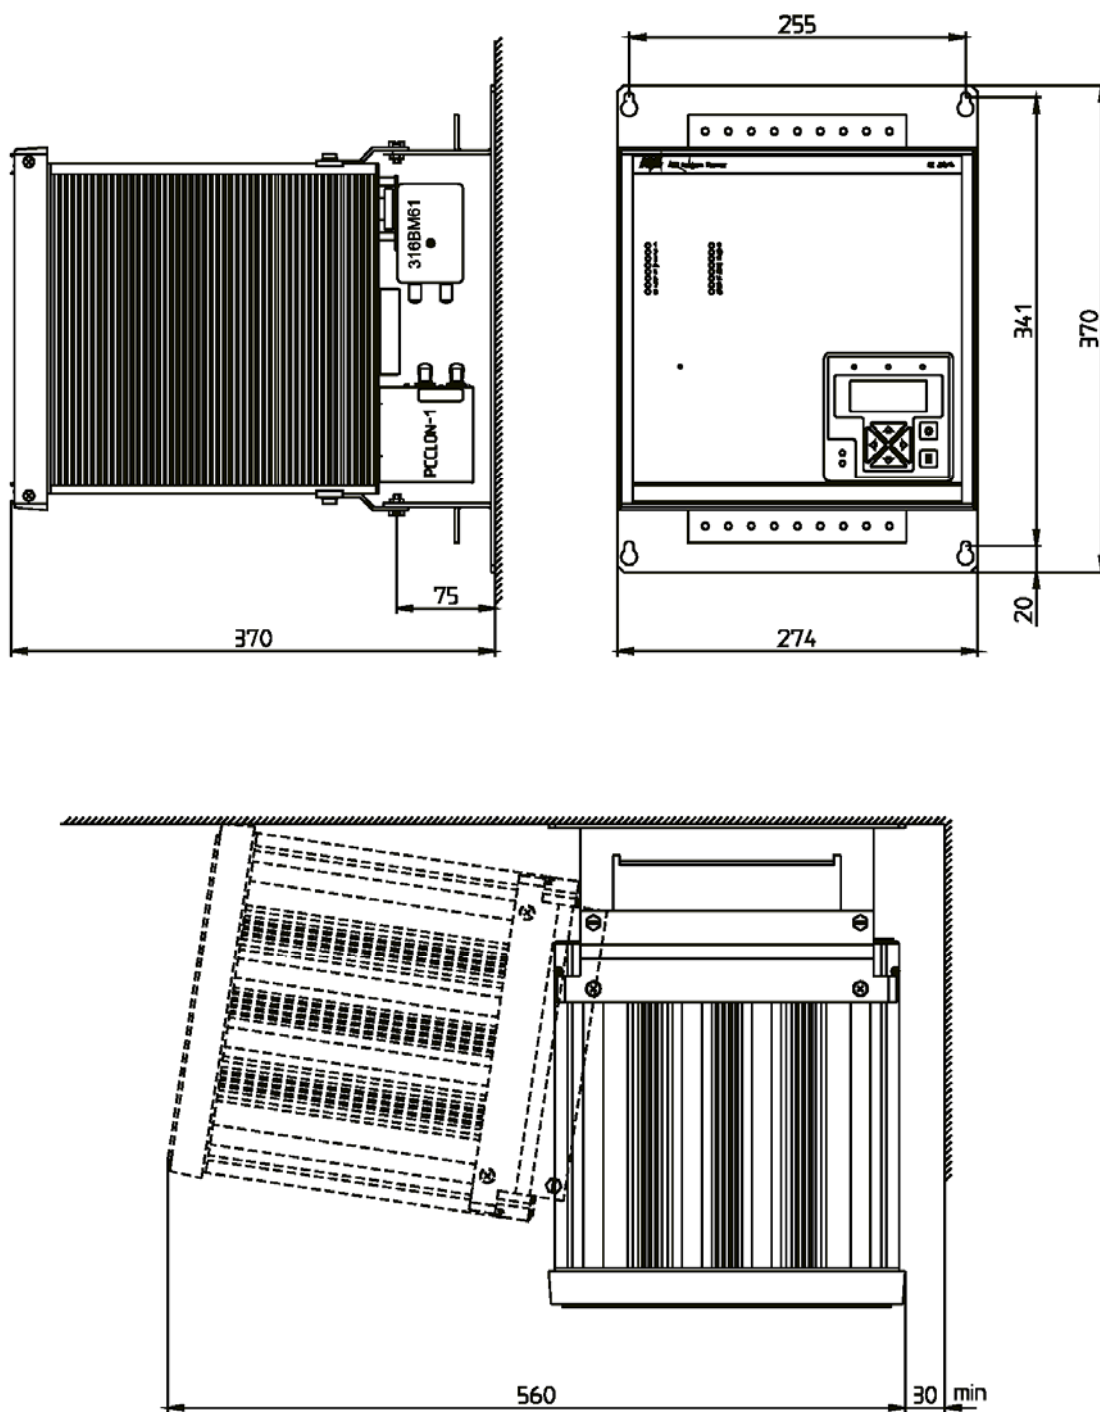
Навесной монтаж, корпус может поворачиваться влево, заднее присоединение, корпус размером N2
